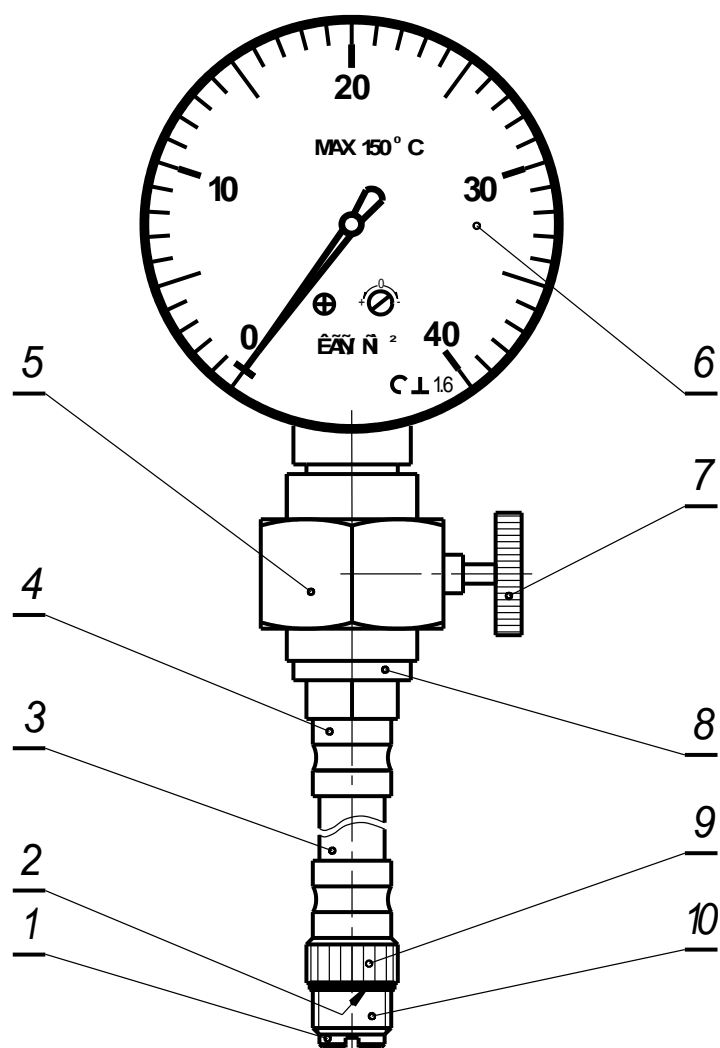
Компрессометр BEST-02DU (общий вид): 1 – седло клапана;
